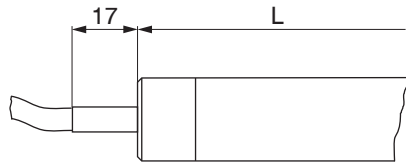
Wegsensor Typ - CA mit integriertem Kabel
